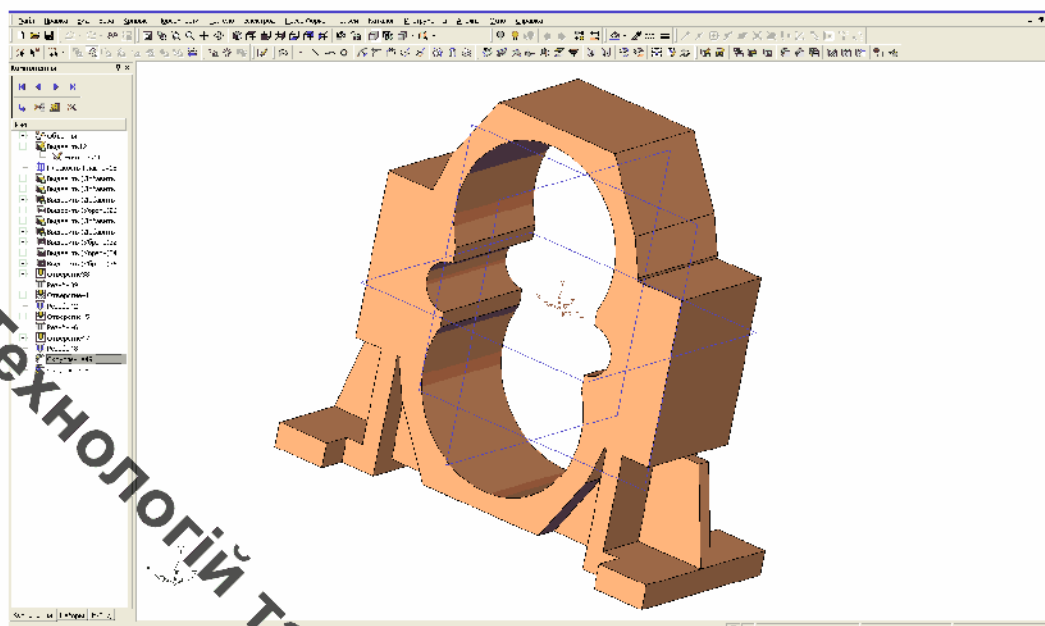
Створення основи та корпусу деталі «Корпус В.25»
